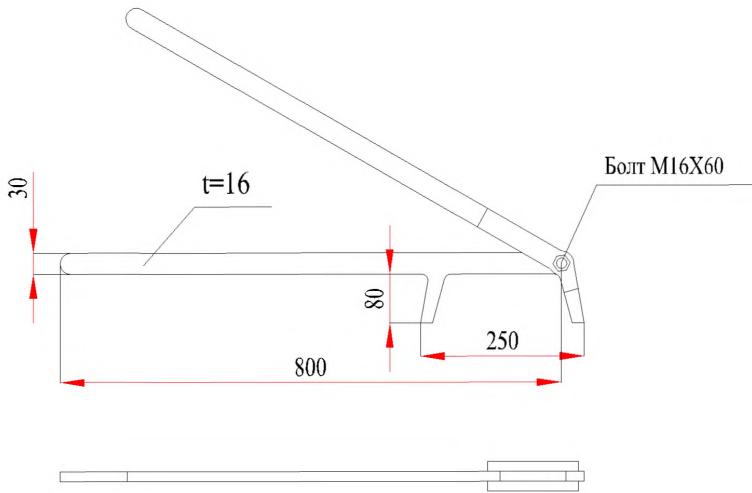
Приспособление для сборки трубы фундамента со стойкой анкерно-угловой и концевой опор
